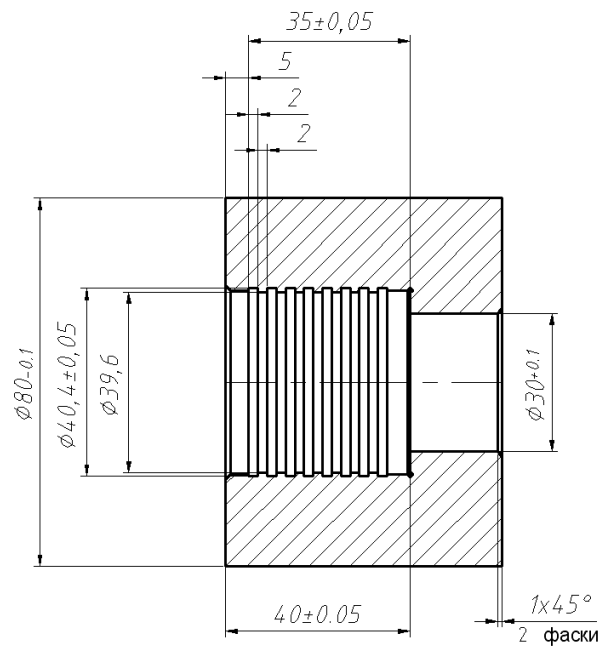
Эскиз корпуса из стали 12ХН3А с прямоугольным профилем.
